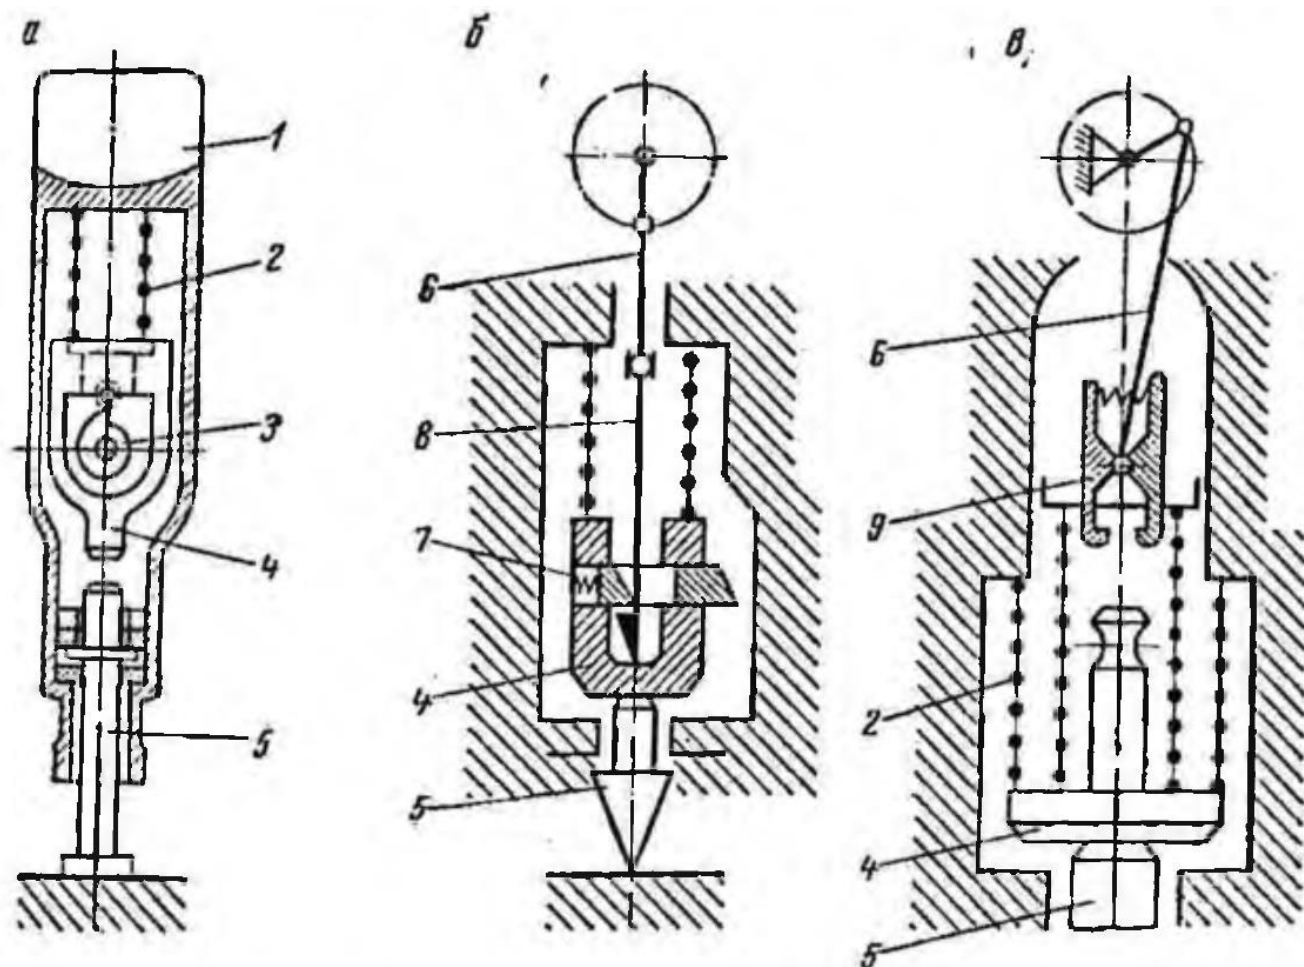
Схеми пружних ударних механізмів з жорстким зв'язком бойка [13]: 1 - корпус; 2 - пружина; 3 - кулачковий механізм; 4 - боек; 5 - робочий інструмент; 6 - кривошипно-шатунний механізм; 7 - клямка; 8 - шток; 9-захват
